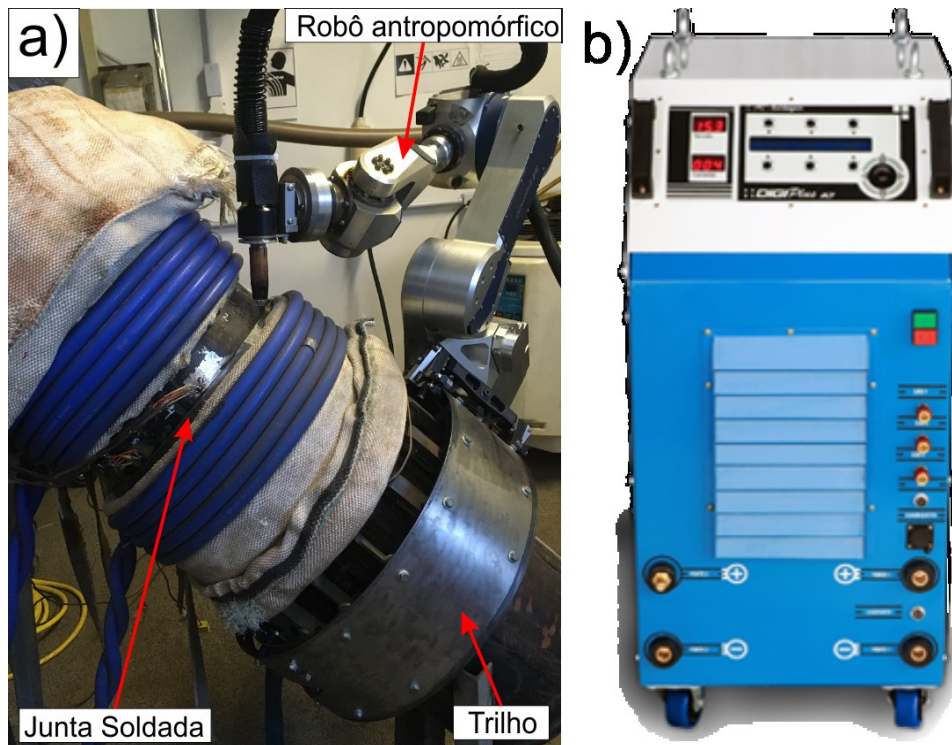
Equipamentos para soldagem. Em a) Bancada para soldagem em operação com robô antropomórfico de 6 eixos em trilho; b) Fonte de soldagem Digipius A7.
